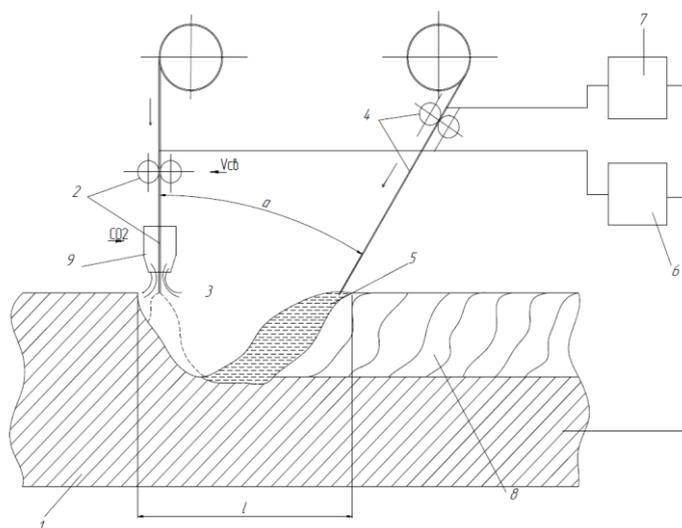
«Схема процесса сварки с ДГП в защитном газе: 1 – изделие; 2 – электрод; 3 – дуга; 4 – ДГП и механизм её подачи; 5 – сварочная ванна; 6 и 7 – источники нагрева; 8 – сварной шов; 9 – газовая защита; α – угол наклона ДГП» [19]
